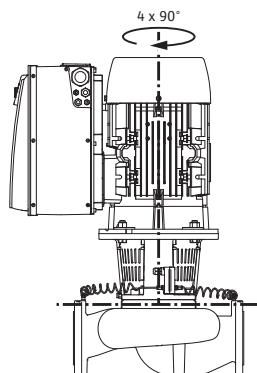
Tilladte installationspositioner med lodret motoraksel
